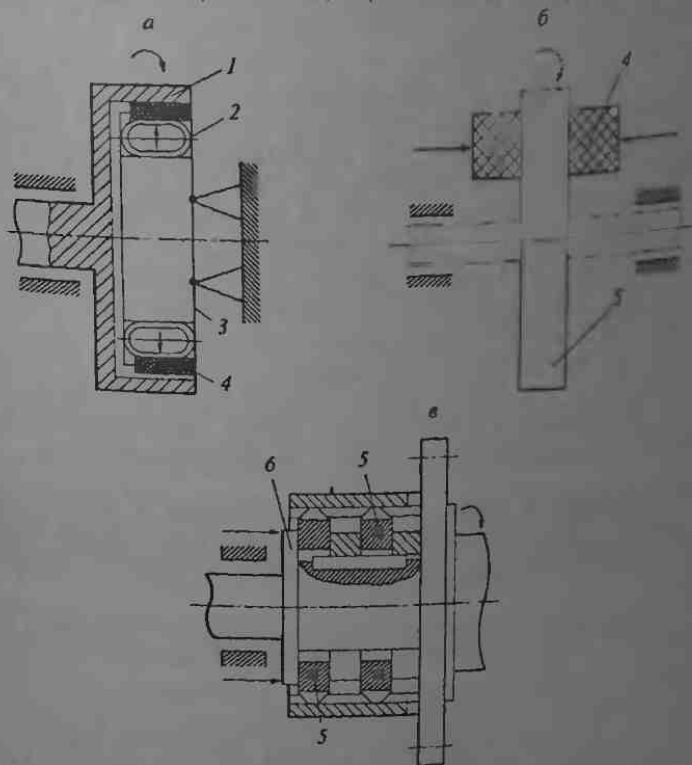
Камерный (а), однодисковый (б) и многодисковый (в) тормоза: 1 — барабан; 2 — камера; 3 — корпус; 4 — колодки; 5 — диски; 6 — корпус, соединенный с неподвижными дисками (по Чичингадзе и Брауну)
